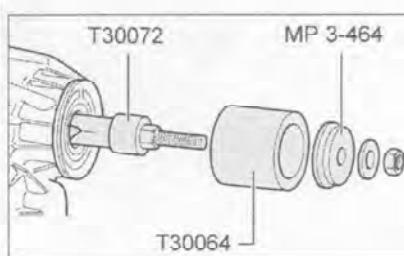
Извлеките внутреннюю обойму подшипника входного/первичного вала.
